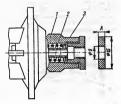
Установка дополнительной шайбы в вакуумный регулятор: 1 — корпус; 2 — пружина; 3 — дополнительная шайба; А — толщина
